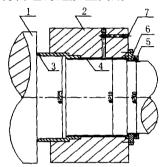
改造前轴承体结构图 1 報筒; 2 轴承体; 3 定位套; 4 滑动轴承;
